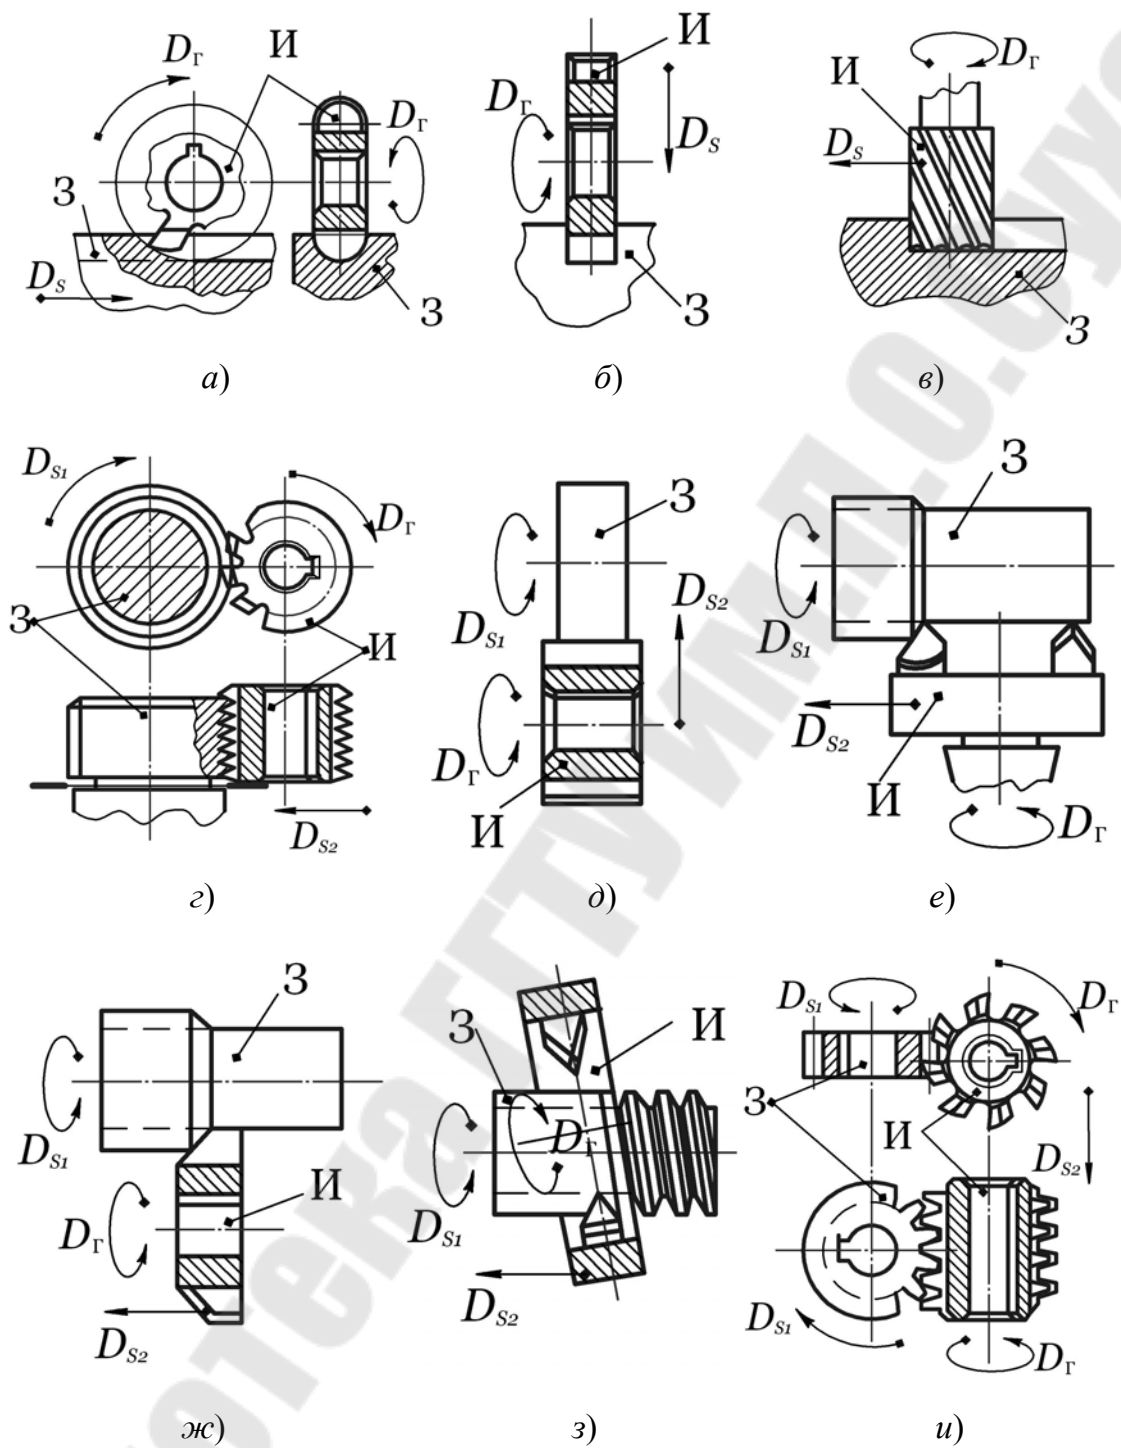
Способы фрезерной обработки: фрезерование канавок (а), отрезание (б), фрезерование пазов концевой фрезой (в), резьбофрезерование гребенчатой фрезой (г), врезное фрезерование (д), круговое фрезерование торцевой фрезой (е), круговое фрезерование дисковой фрезой (ж), вихревое нарезание резьбы (з) и зубофрезерование (и)
